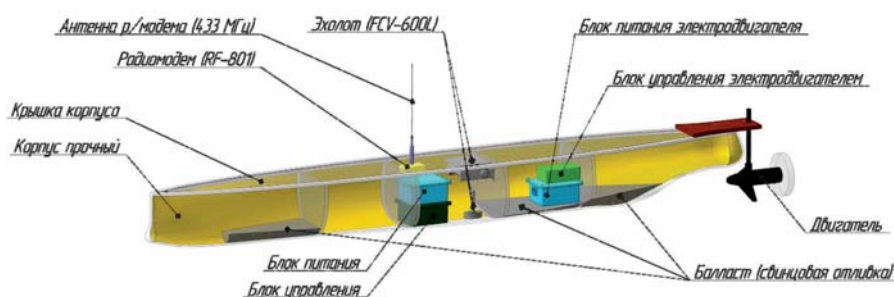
Общий вид макета СмТК и компоновка бортового оборудования
